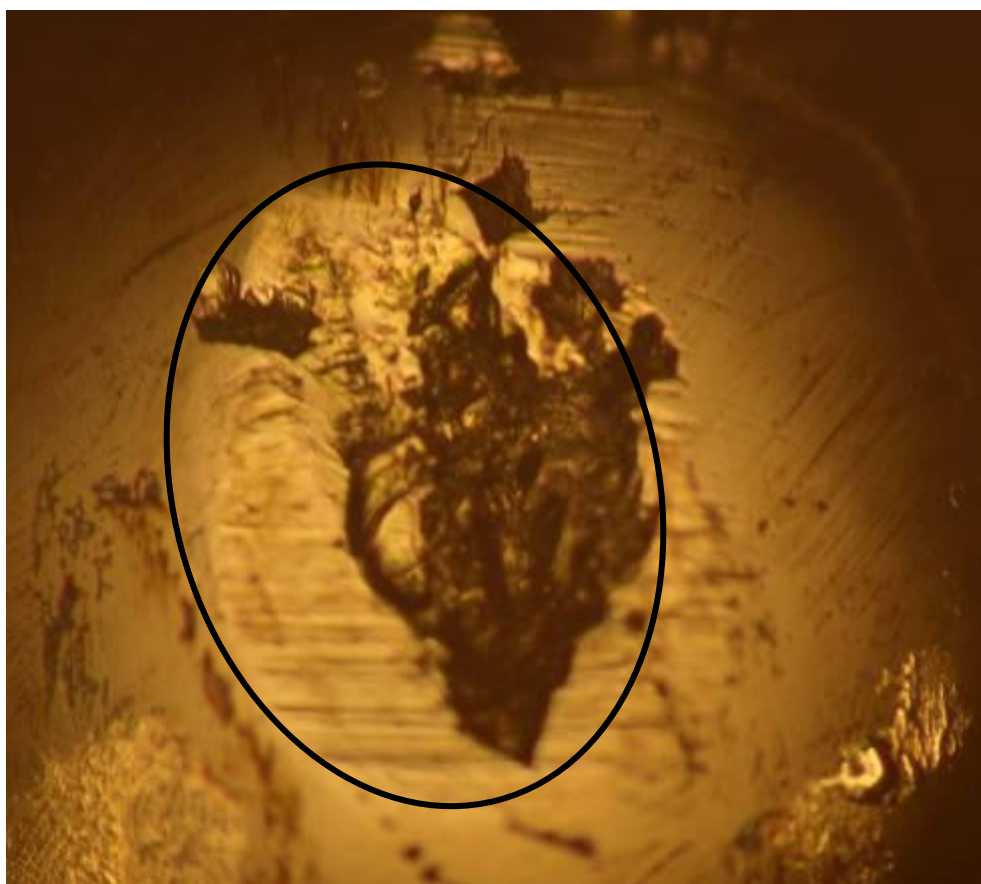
Фото рабочей части инструмента с зоной пластической деформации
